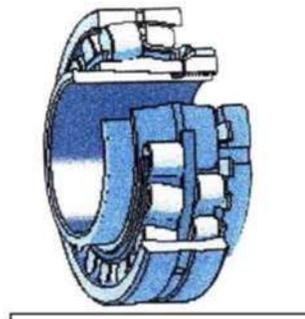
Rodamiento de rodillos a rótula SKF.
